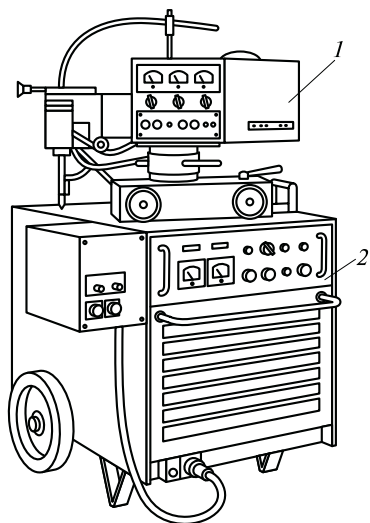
Сварочный автомат АДГ-502:
